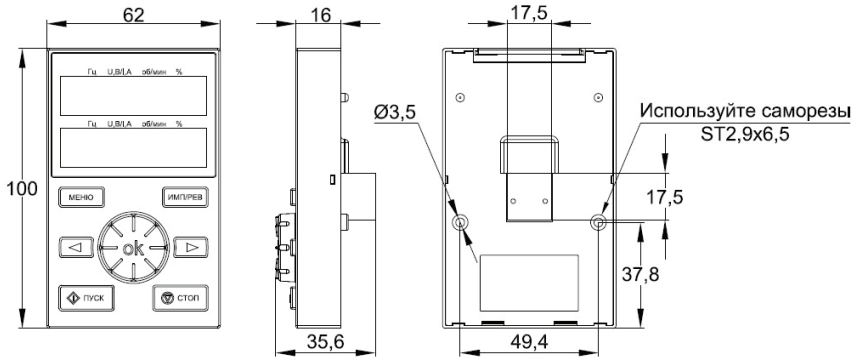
Габаритные размеры и размеры отверстий внешней цифровой двухстрочной панели управления (единица измерения - мм)
